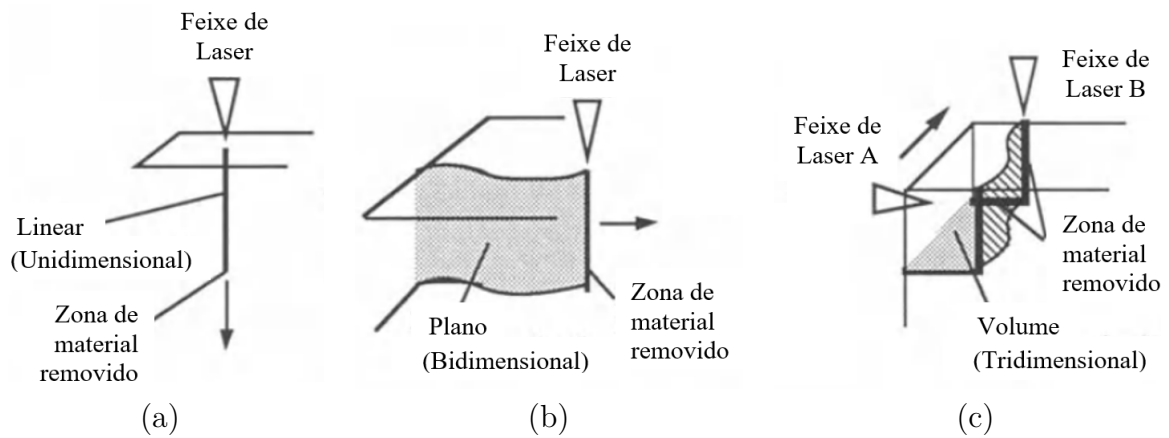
Representação esquemática para processos (a) uni, (b) bi e (c) tridimensional de usinagem a laser. Fonte: adaptado de Chryssolouris, Sheng e Alvensleben (1991)
